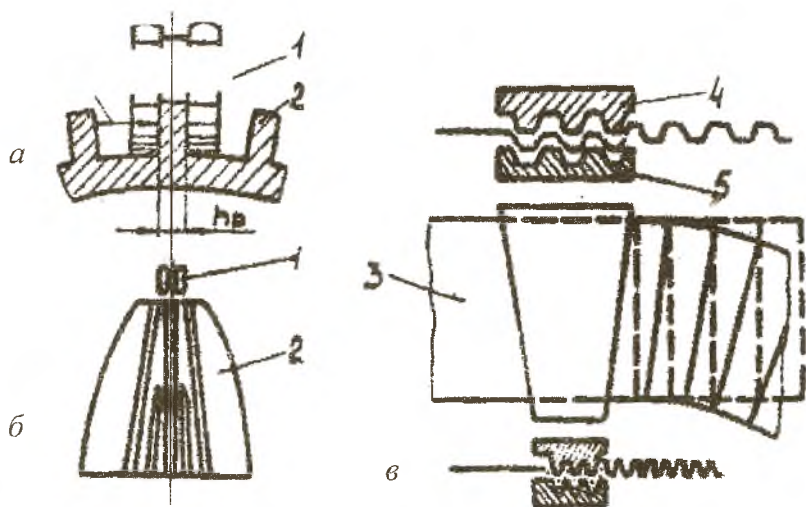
Схемы фрезерования канавок на наружной поверхности стенки (а), удвоения ребер (б) и штамповки гофров (в): 1 – фреза; 2 – ребро стенки; 3 – заготовка для гофрирования; 4 – матрица; 5 – пуансон
